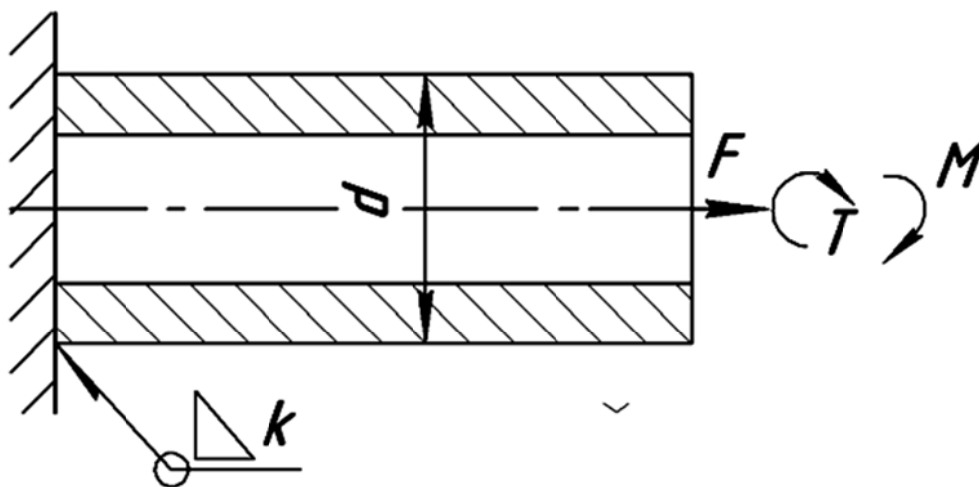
Соединение трубы с плитой методом сварки
